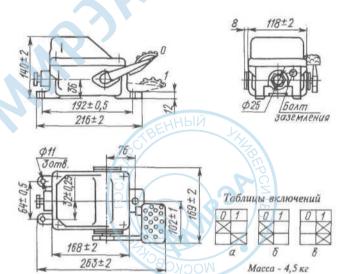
Габаритные, установочные размеры и масса выключателя типа HБ-741
